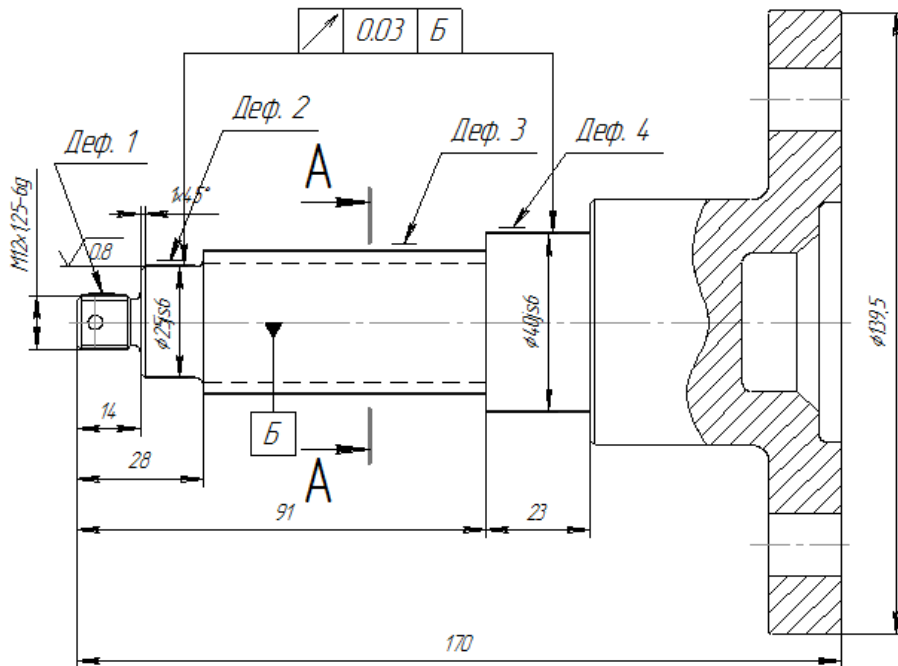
Ремонтне креслення вала з фланцем УКЕ–41
